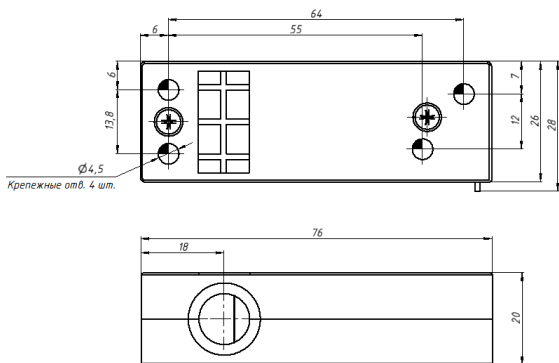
Габаритные и установочные размеры замка Promix-SM.420.10
